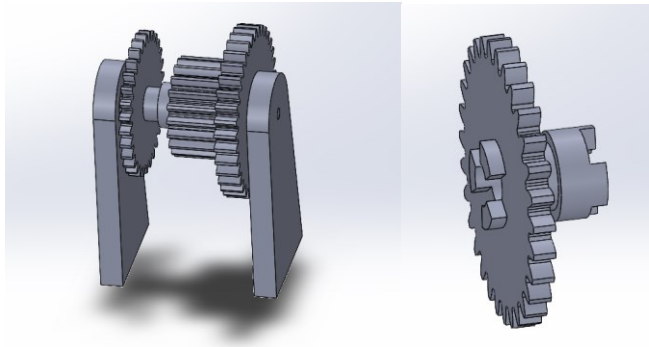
Shifting Gear 齒輪組 Solidworks 模型
